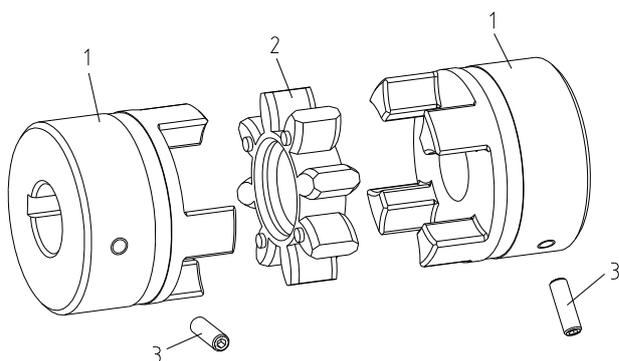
ROTEX® GS, типоразмеры 5 - 38
